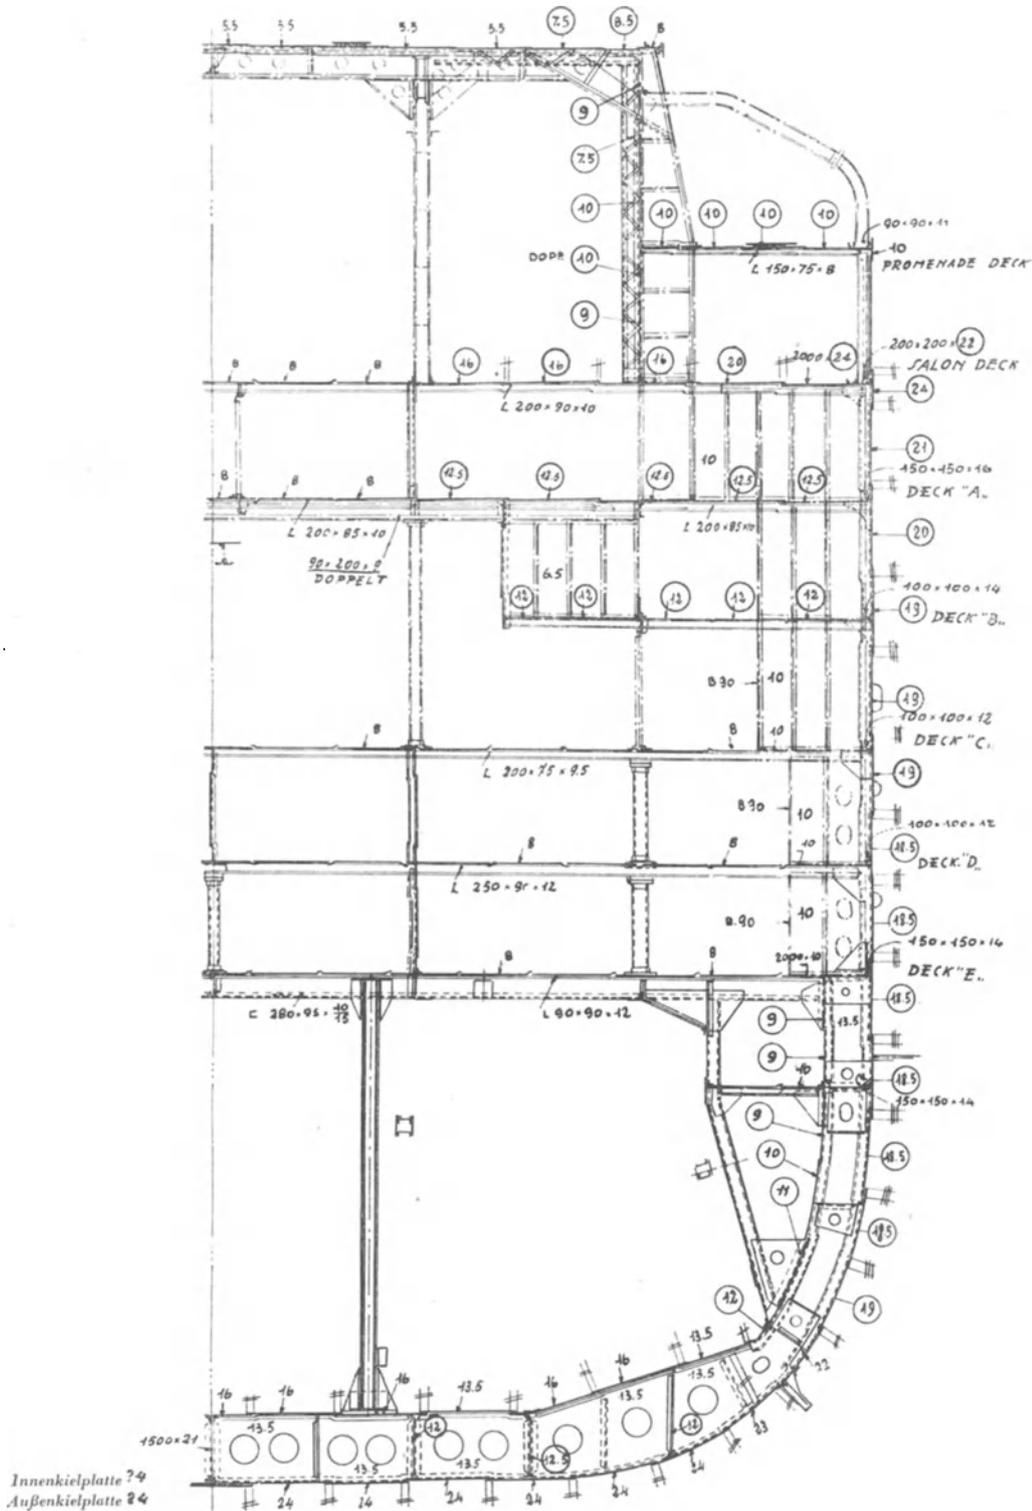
a Vierschrauben.Turbinendampfer „Conte di Savoia“; Hauptspant
